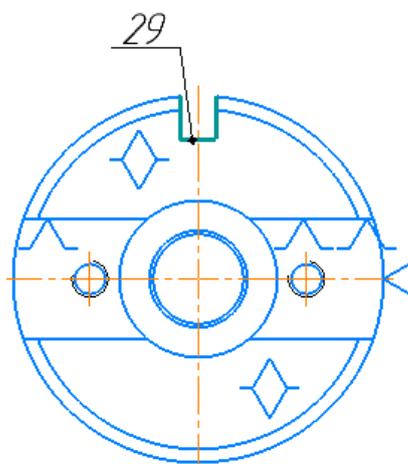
Эскиз вертикально-фрезерной операции
